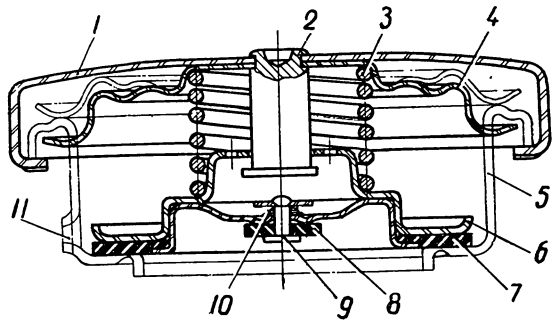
Пробка горловины водяного радиатора: 1 — корпус пробки; 2 — стержень; 3 — пружина выпускного клапана; 4 — пружина и уплотнительная шайба; 5 — заливная горловина; 6 — корпус клапанов; 7 — резиновая прокладка выпускного клапана; 8 — резиновая прокладка впускного клапана; 9 — впускной клапан; 10 — пружина впускного клапана; 11 — отверстие для подсоединения паропроводящей трубки
